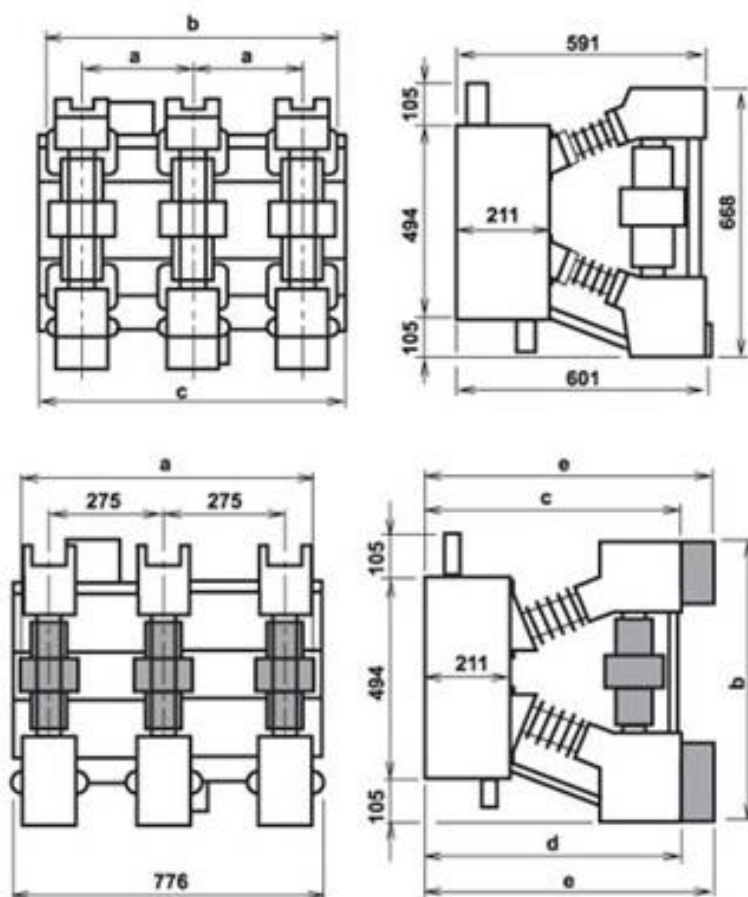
Общий вид и габаритные размеры выключателя типа ВВСТ-3АН1
